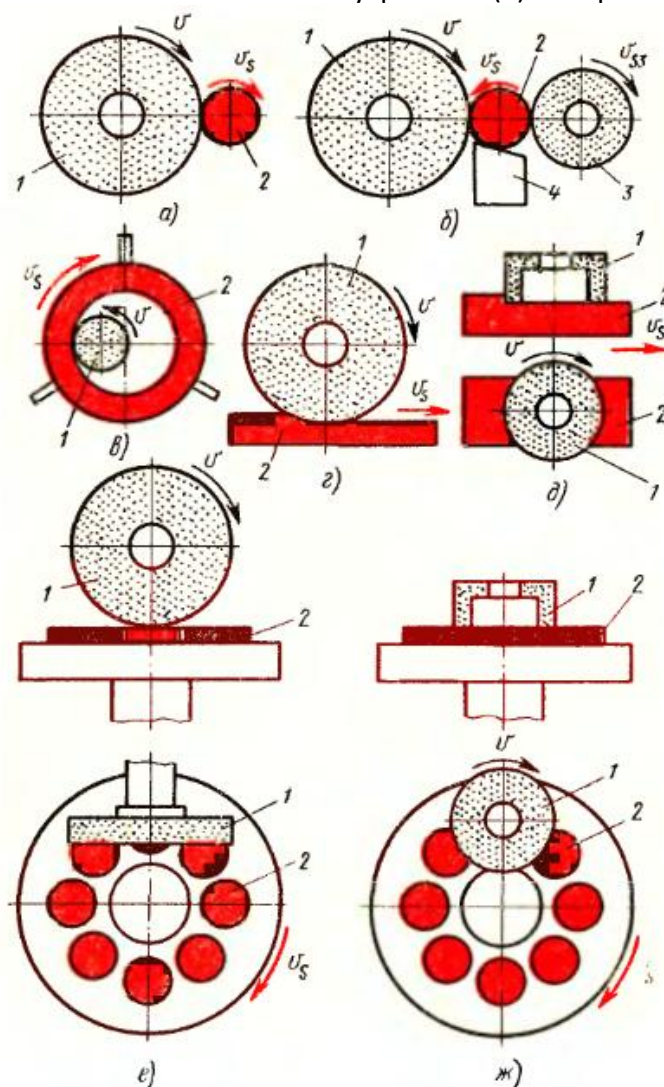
Схемы расположения круга и заготовки и направления движения подачи при шлифовании периферией круга (а, б, е, г, е) и торцом круга (д, ж):
